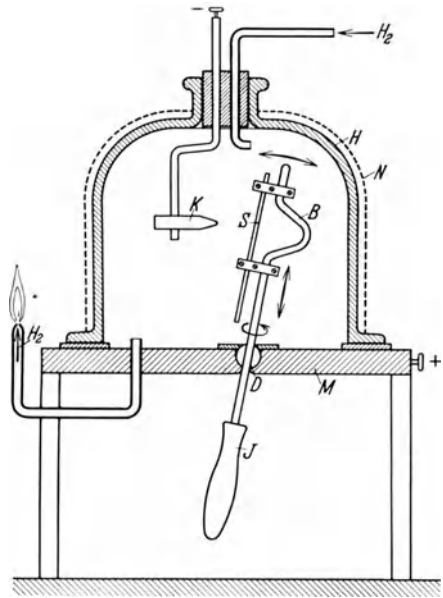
Schweißen mittels Gleichstromlichtbogen und Kohlelektrode unter einer Haube mit H₂-Schutzgas. K Kohle; S Schweißstelle; B Werkstückhalter, allseitig schwenkbar mittels Kugelschliffdichtung D und isoliertem Handgriff I; M Metallgrundplatte; H Haube aus Glas mit Drahtnetzbewehrung N oder aus Metall mit Schauglas.
